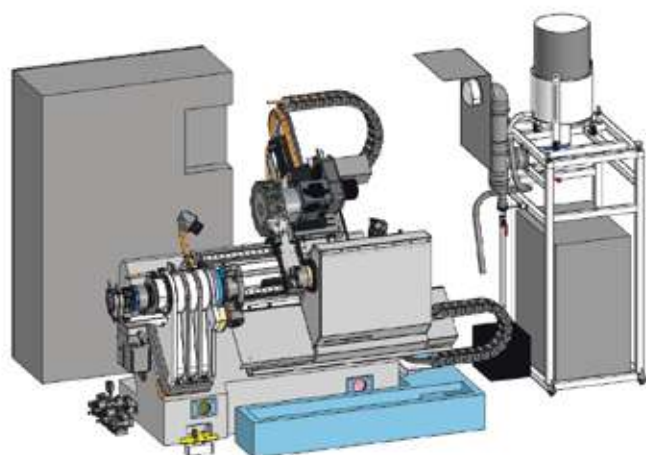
Конструктивная схема ультрапрецизионного токарного станка
